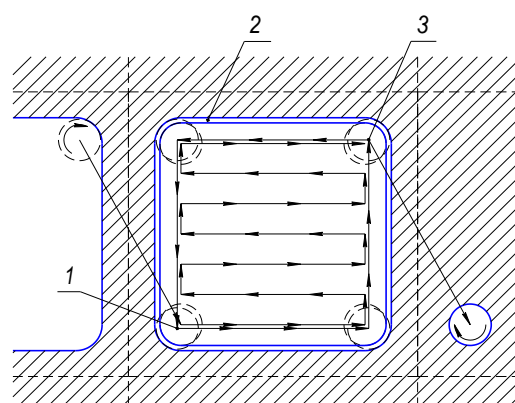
Типичный цикл фрезерования ячейки: 1 – начало обработки (врезание); 2 – слой обработки по контуру; 3 – конец обработки (отвод фрезы).
